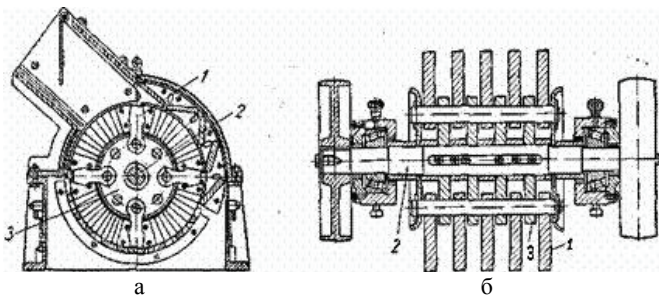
Схематический вид поперечного (а) и продольного (б) сечений молотковой однороторной дробилки. Обозначения на рис.: 1 – молоток, 2 – вал, 3 – внутренний барабан.
